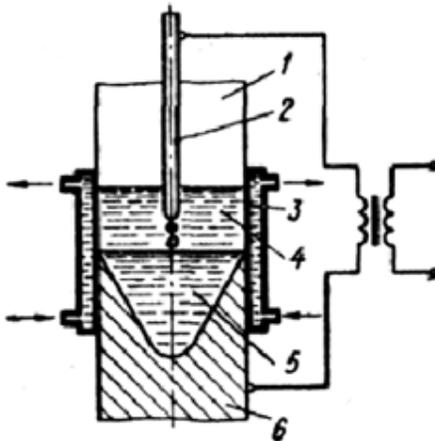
Схема электрошлакового процесса: 1- свариваемые детали; 2 – электрод; 3 – водоохлаждающие формирующие ползуны; 4 – шлаковая ванна; 5 – металлическая ванна; 6 – сварной шов.
